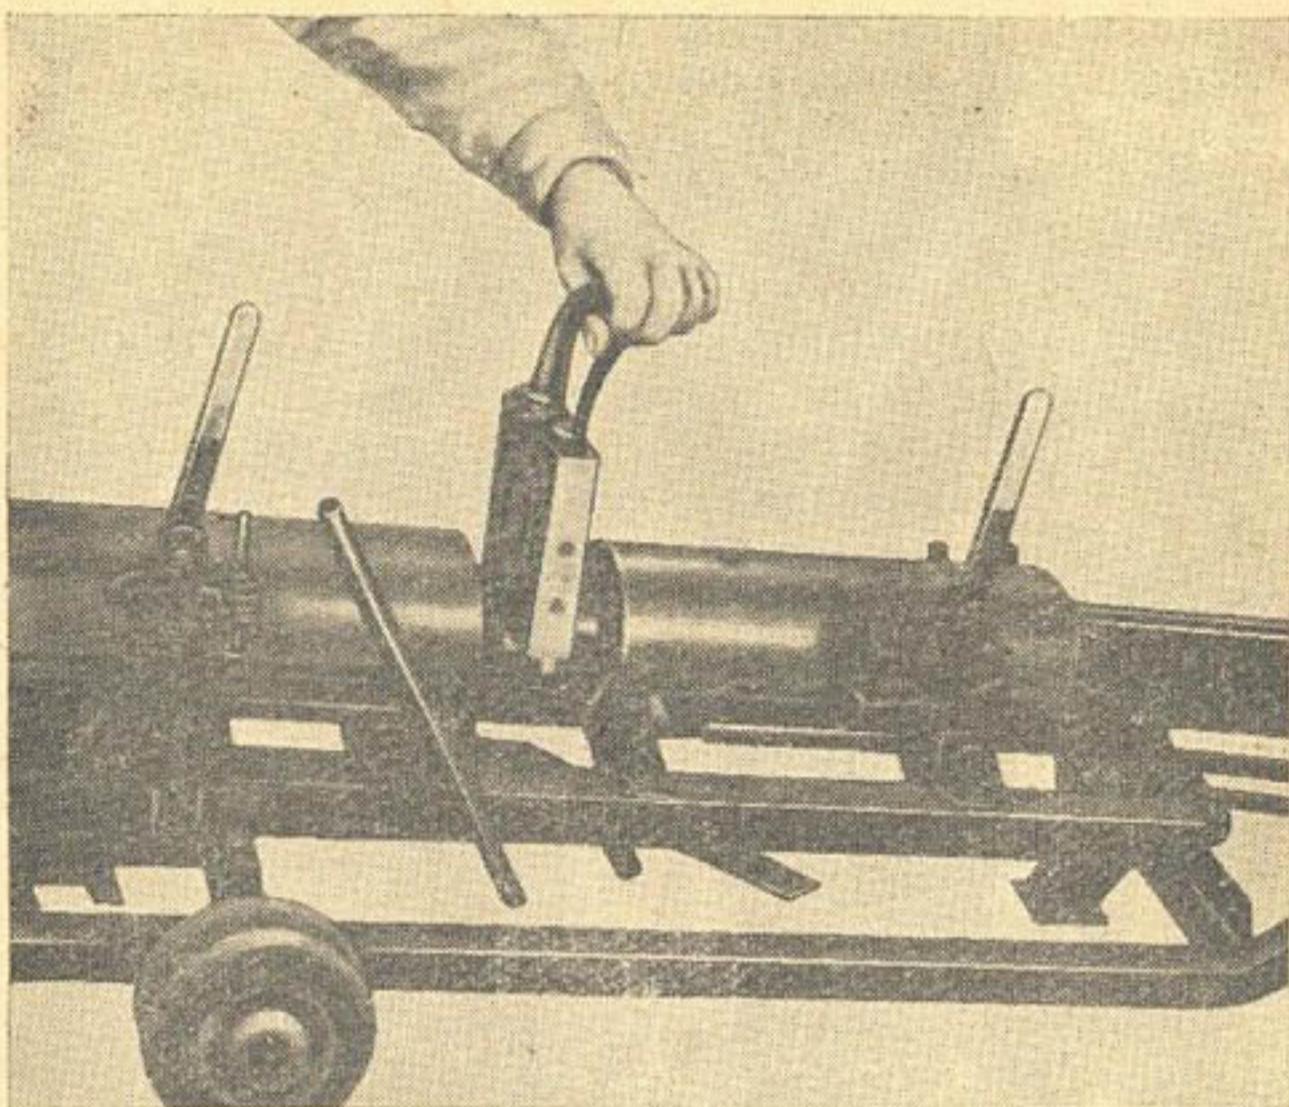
Установка для сварки полиэтиленовых труб компании «Филлипс Петролеум».
